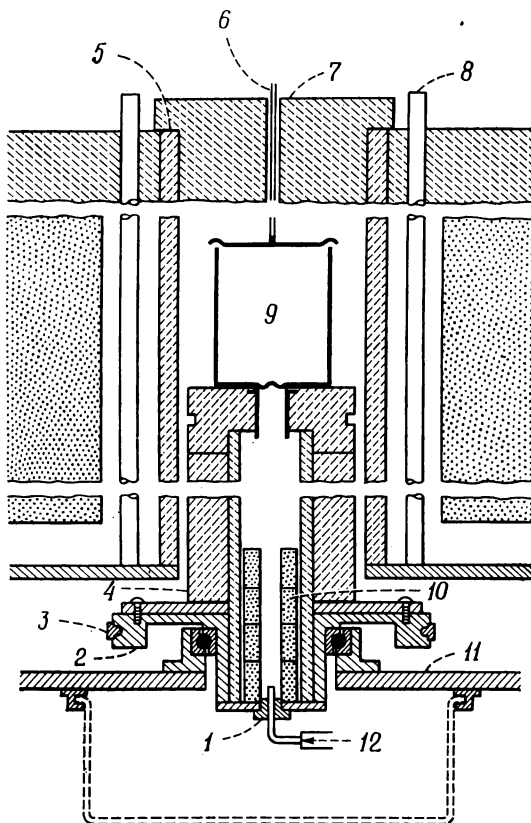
Конструкция печи, пьедестала и тигля для выращивания кристаллов [52].
